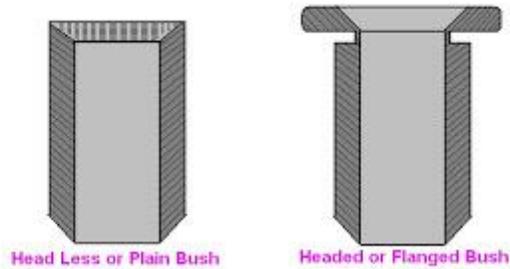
Press Fit Wearing Bushes. Fuente: American Machinist
